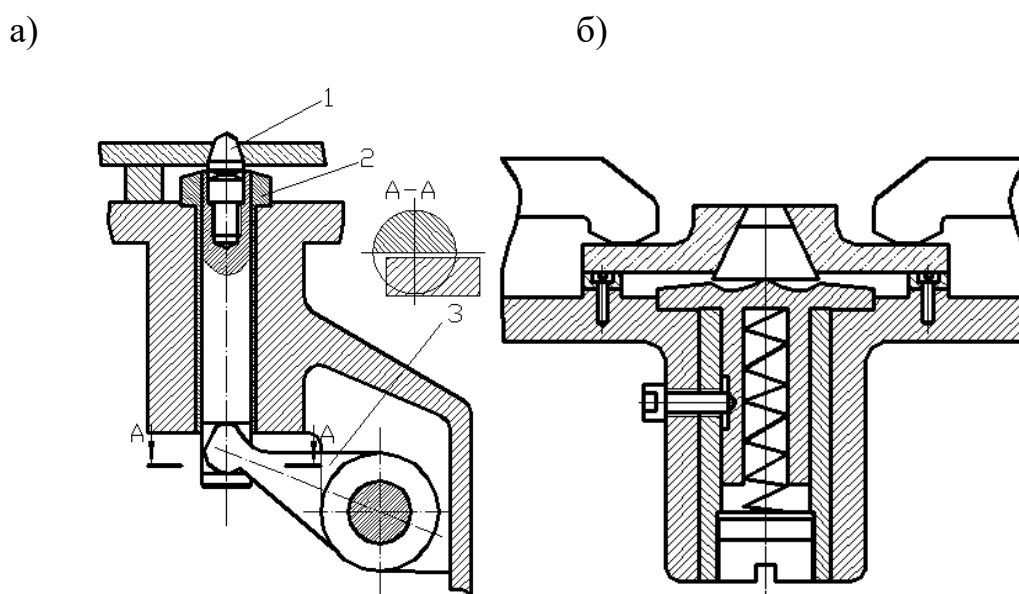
Примеры базирования заготовок на выдвижные пальцы.
